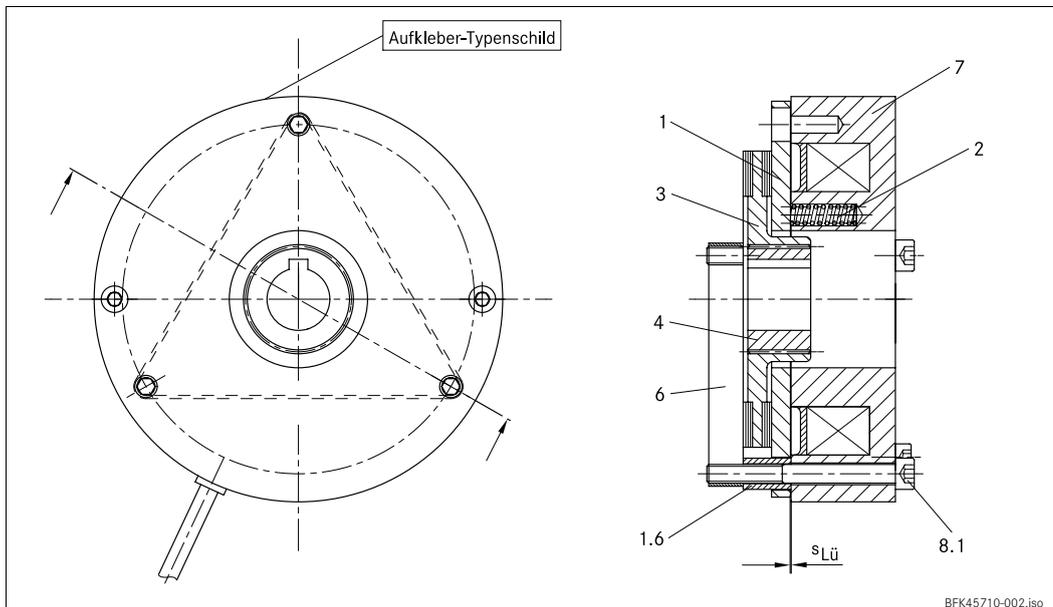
Aufbau einer Federkraftbremse BFK457-06...16 Basic, Magnetteil komplett mit Rotor
